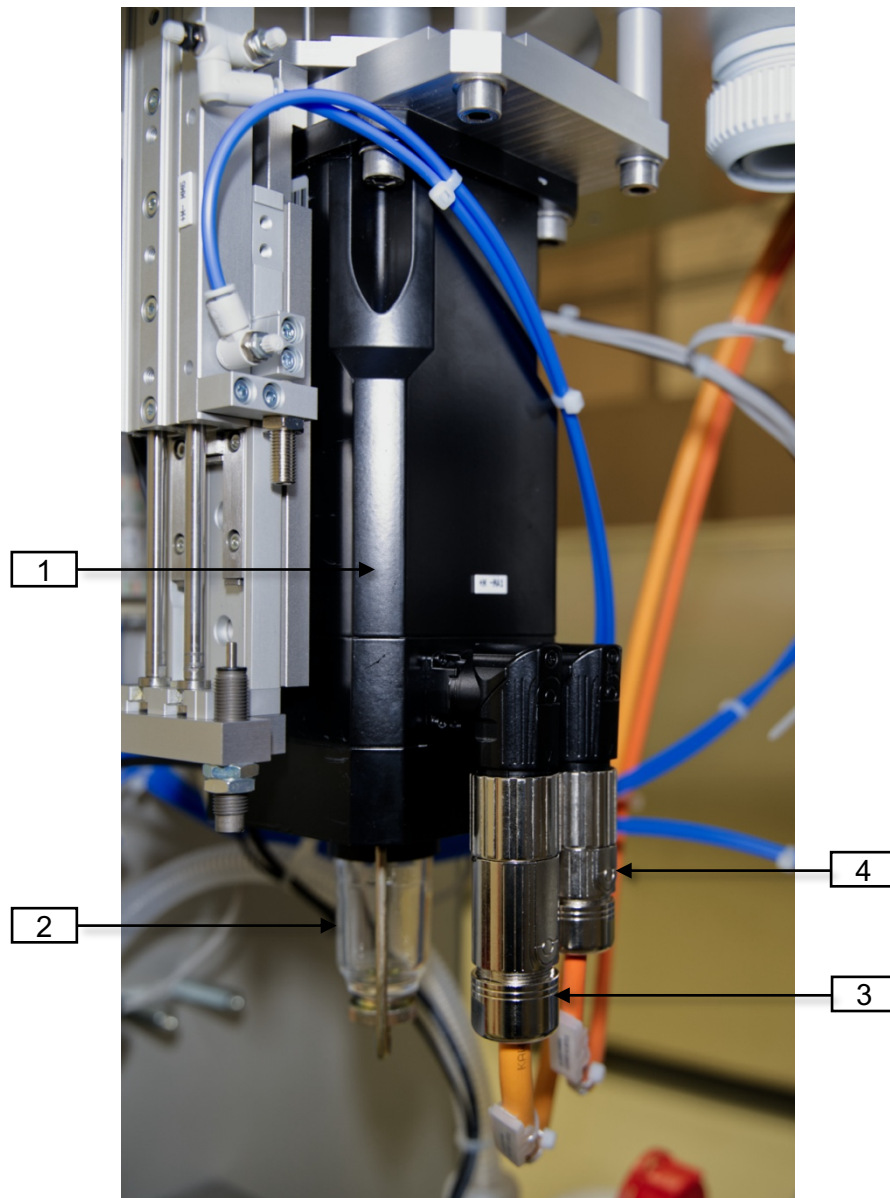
Drehtellermotor mit Vakuumschauglas
